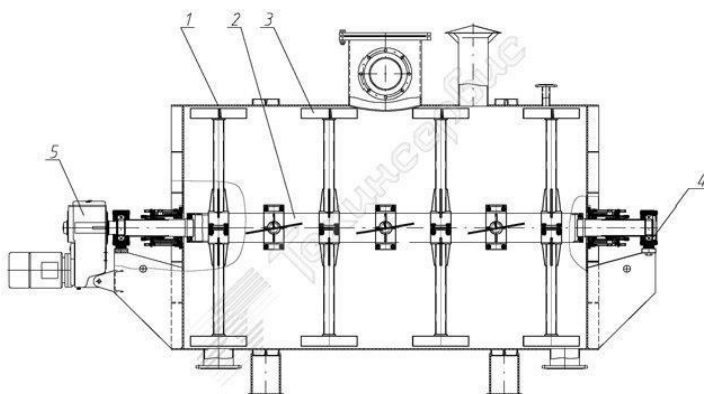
Мішалка -дозатор маточного утфеля МДУ-9
